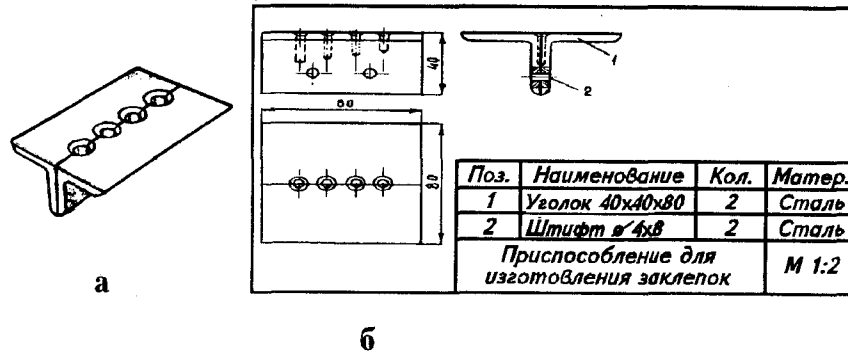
Рисунок (а) и сборочный чертеж (б) приспособления для изготовления заклепок: 1 — уголок; 2 — штифт
